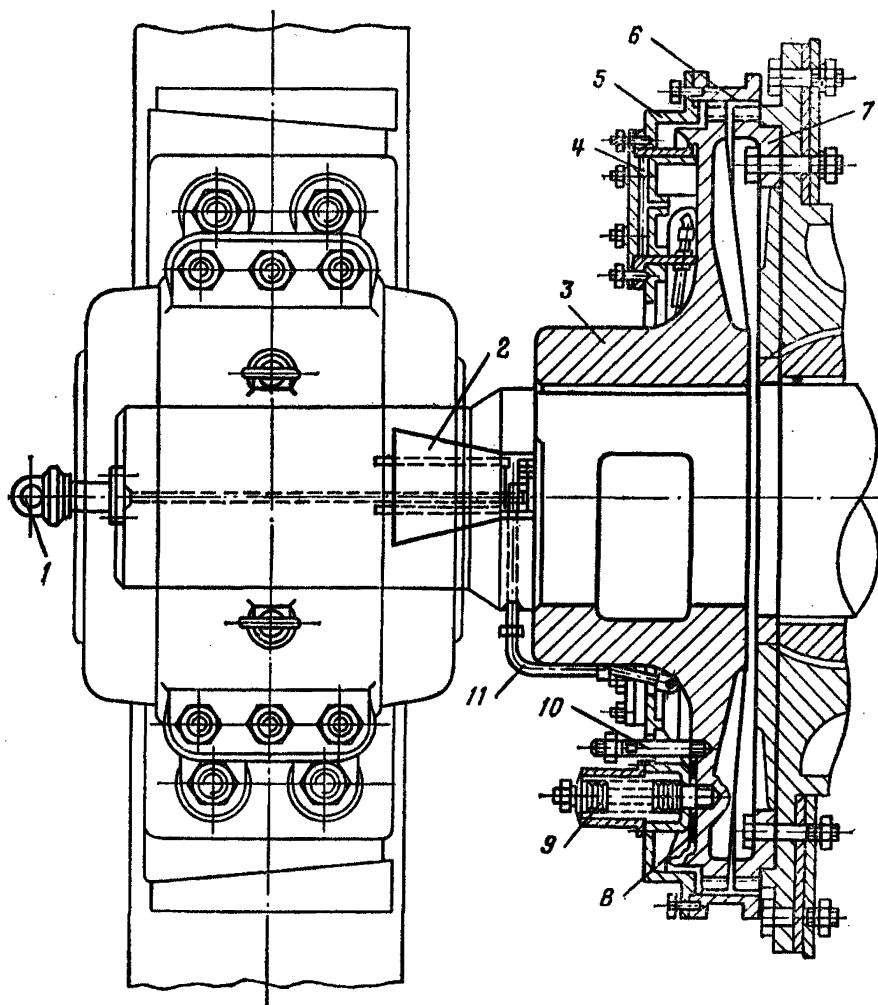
Зубчатый безрычажный механизм перестановки НКМЗ;
